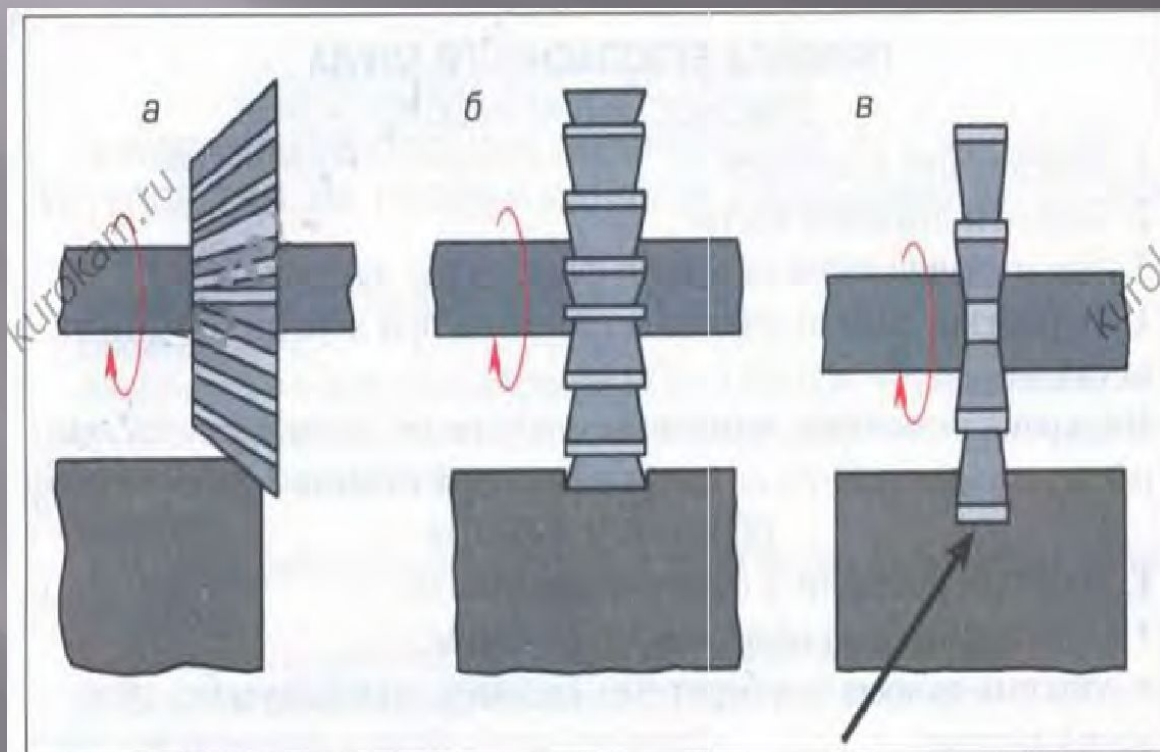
Фрезерование пазов и разрезание заготовок: а – получение скоса, б – прорезание паза, в – разрезание заготовки
